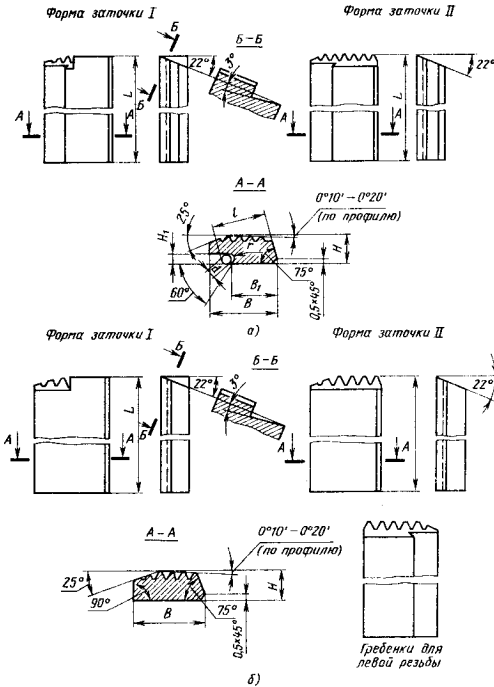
Резьбонарезные плоские гребенки: а — тип А; б — тип Б (размеры см. табл. 129).
